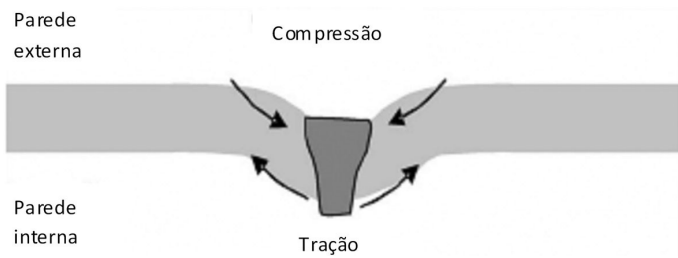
Efeito torniquete em tubos soldados [2].
